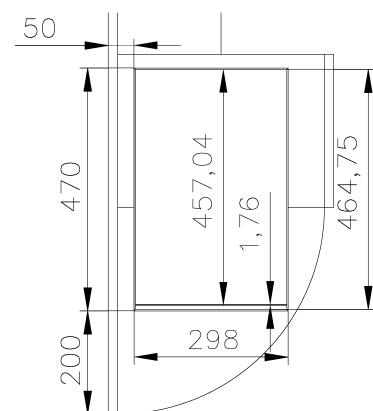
▼ Основные размеры сканера и расположение его на чертеже рабочей зоны
